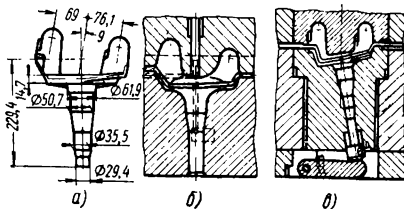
Штамповка поворотного кулака автомобиля ГАЗ: а — поковка; б — первый переход; в — второй переход
